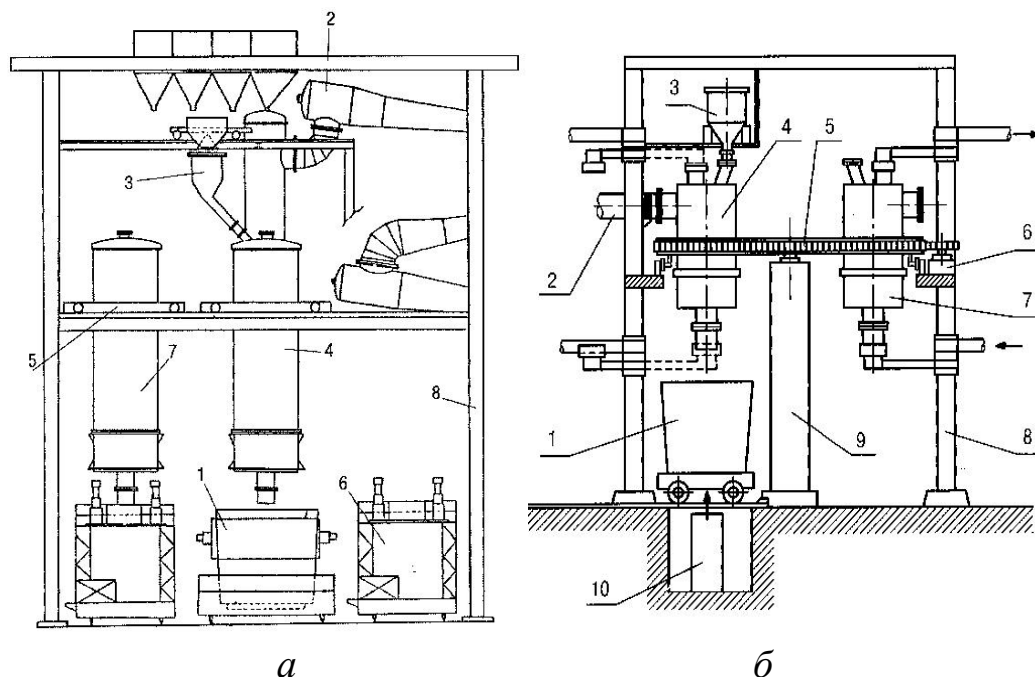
Двухпозиционный циркуляционный вакууматор с тележками для перемещения вакуум-камеры (а) и с поворотной платформой: 1 — ковш; 2 — вакуумный насос; 3 — питатель; 4 — рабочая вакуум-камера; 5 а — тележка для перемещения вакуум-камеры; 5 б — поворотная платформа; 6 а — ремонтная тележка; 6 б — привод поворотной платформы; 7 — резервная вакуум-камера; 8 — металлоконструкция; 9 — опора; 10 — механизм вертикального перемещения ковша
